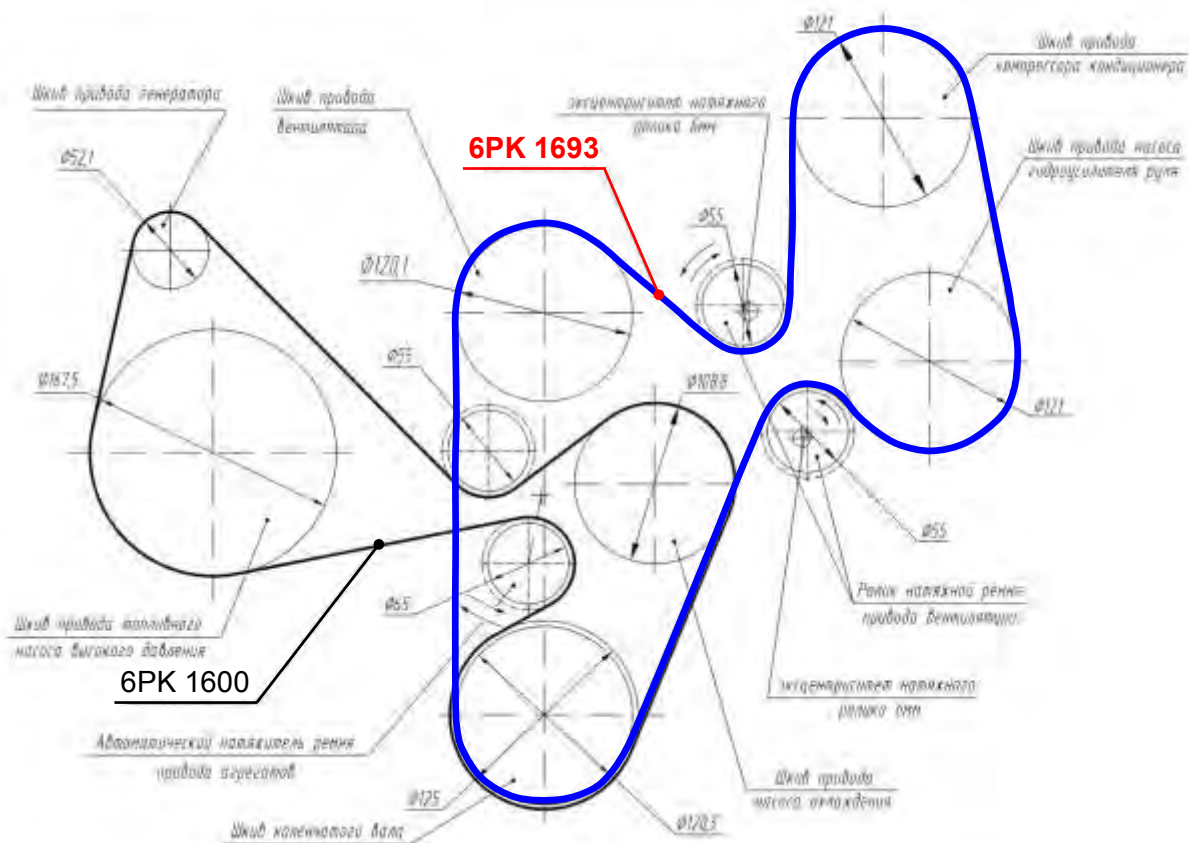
Схема привода вспомогательных агрегатов двигателя для автомобилей на платформе УАЗ-3163 с компрессором кондиционера
